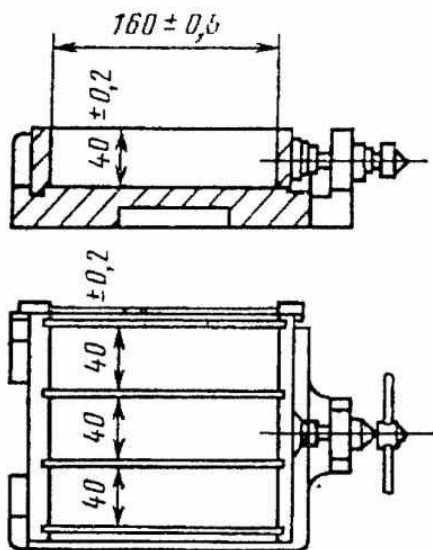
Форма для изготовления образцов-балочек 4x4x16 см
